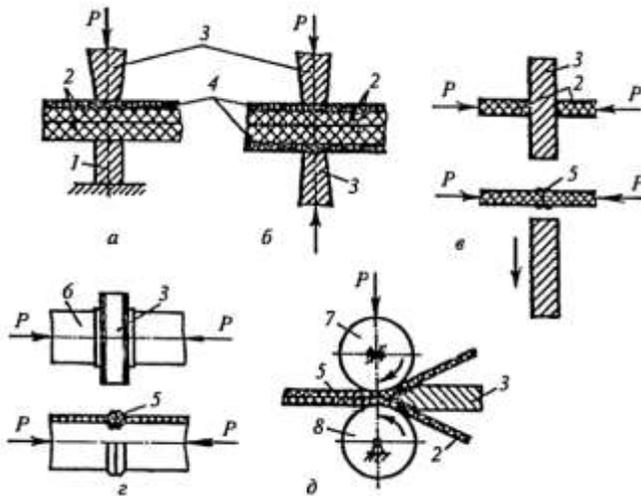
Сварка нагретым инструментом: 1 – опора; 2 – свариваемые листы; 3 – нагретый инструмент; 4 – изоляционная прокладка; 5 – сварной шов; 6 – свариваемые трубы; 7 – ведущий ролик; 8 – ролик-опора
